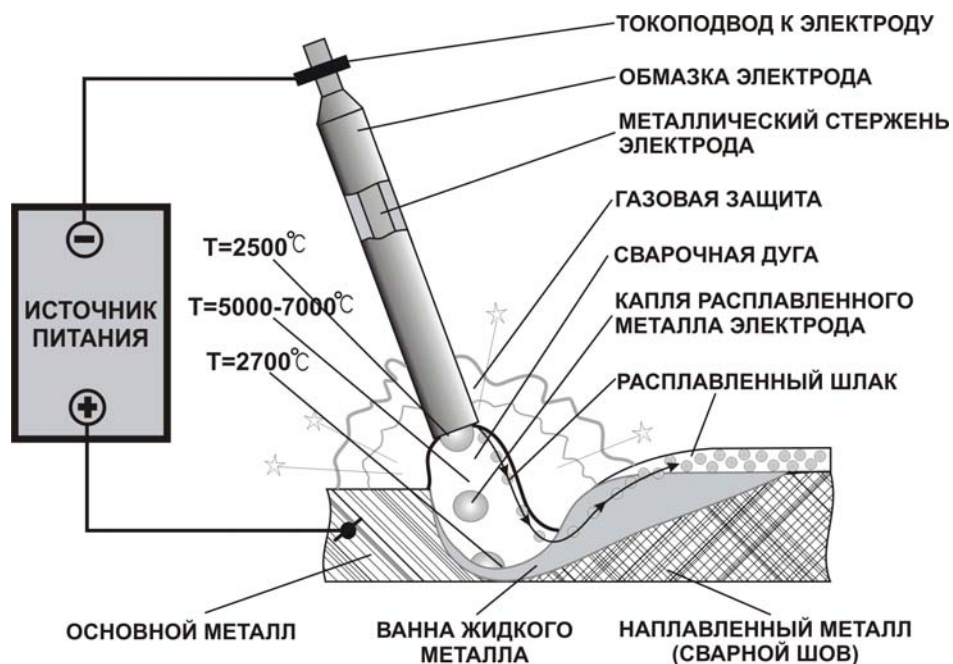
Схема процесса ручной электродуговой сварки
